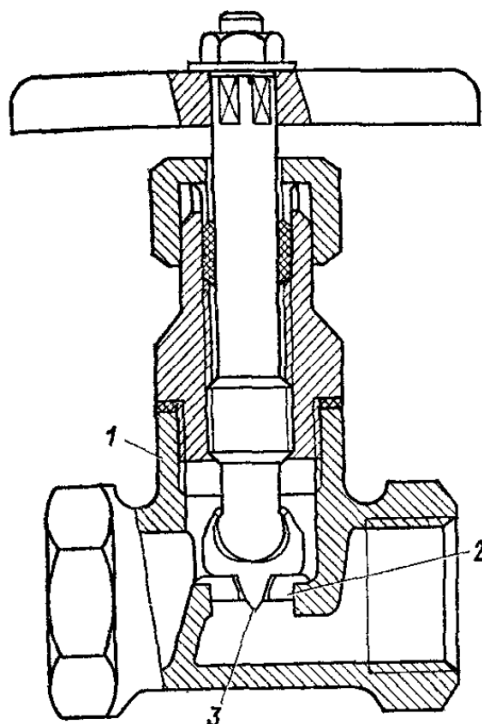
Край регулирующий с дросселирующим устройством: 1 – сборка корпуса муфтового запорного вентиля со шпинделем, крышкой, накладной гайкой и рукояткой; 2 – калиброванная диафрагма; 3 – запорно-регулирующий клапан
